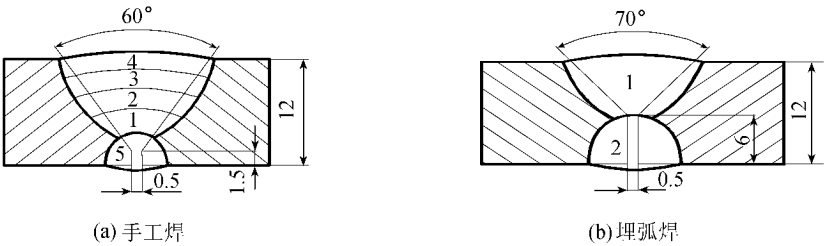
焊接接头简图(尺寸单位:mm)
